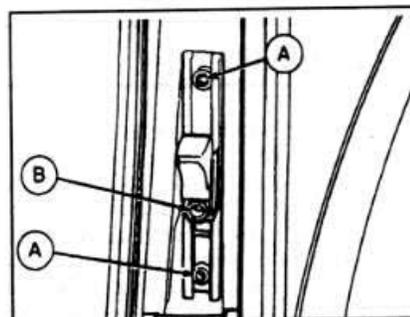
Расположение болтов крепления регулятора высоты ремня (А) и болт верхнего крепления ремня (В).
